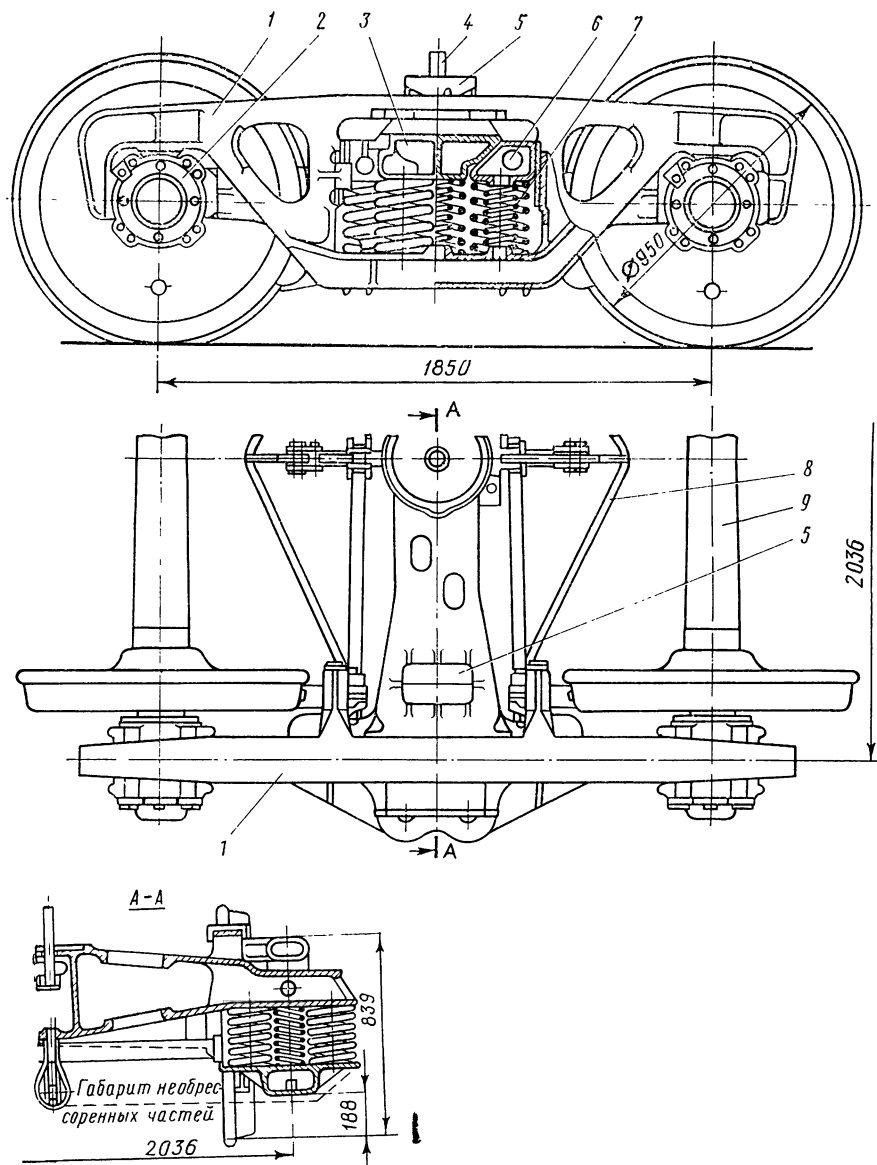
Тележки ЦНИИ-ХЗ-О с буксами на роликовых подшипниках
